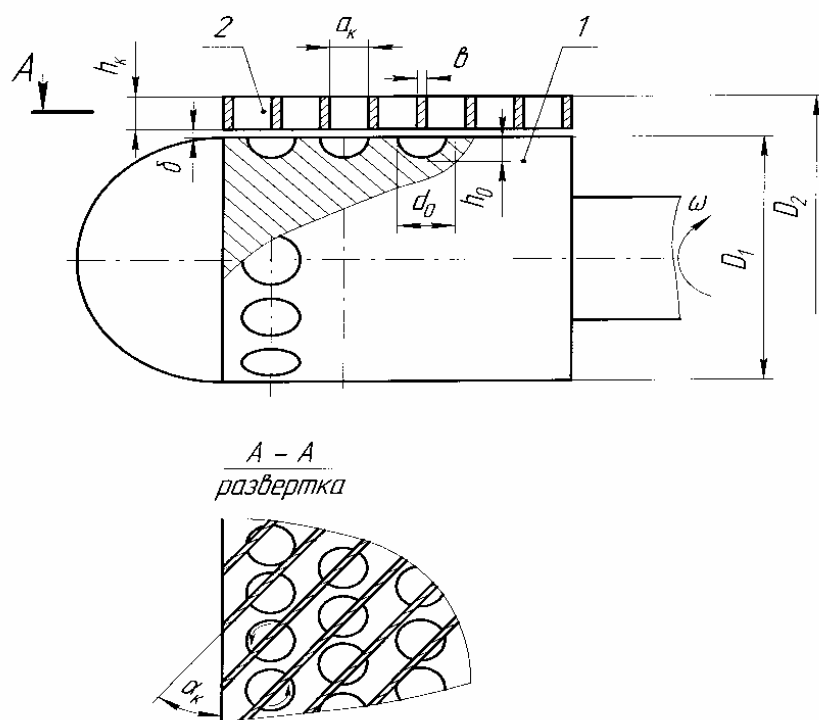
Схема вихревой гидромашины с цилиндрическим ротором и неподвижными винтовыми каналами:
